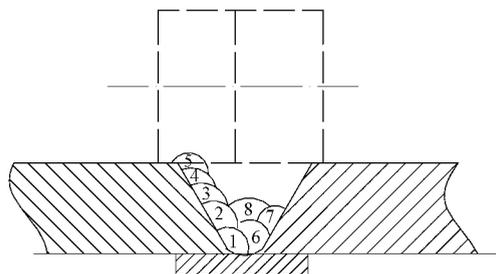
带背面垫板的对接焊缝的焊接示意图
